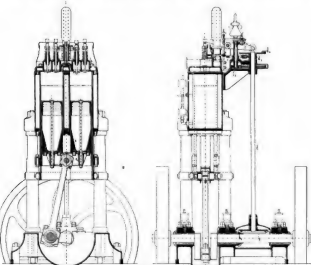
Zwillings-Gasmotor der Griffin Engineering Co., Bath.
